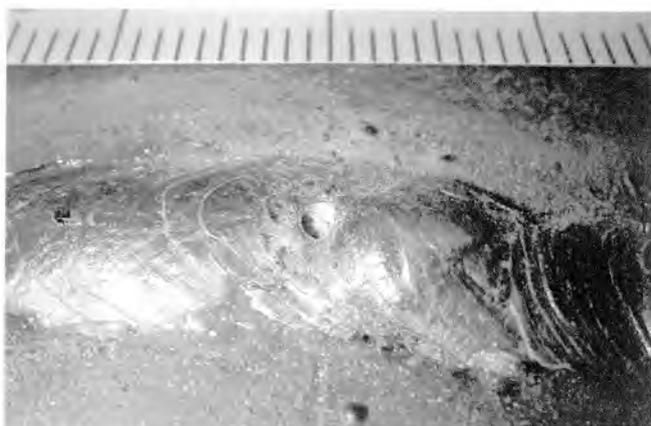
Пора в стыковом сварном соединении трубопровода
